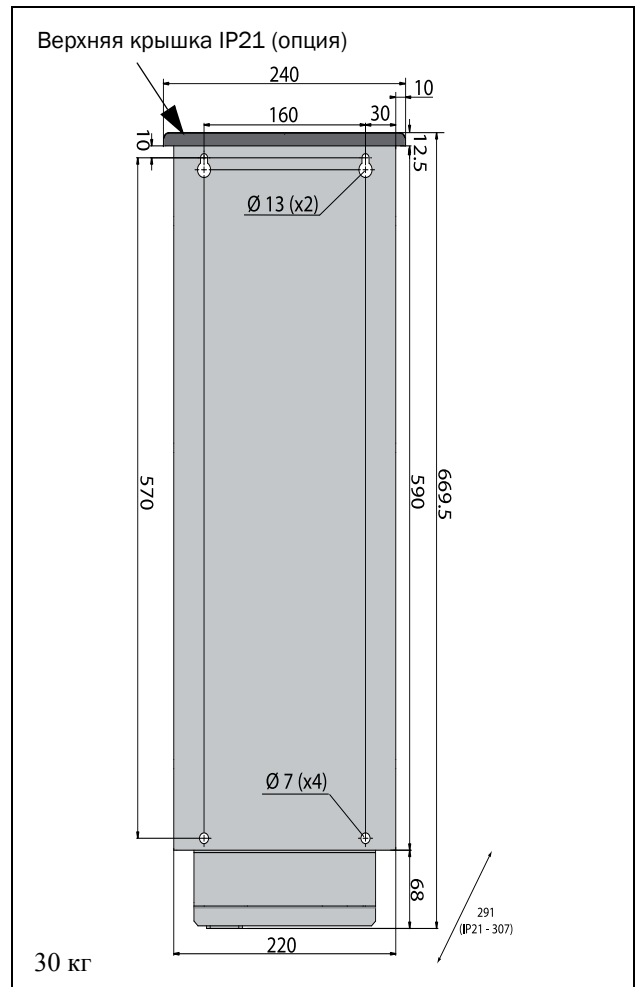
Устройство Emotron FDU моделей от 48-060 до 48-088 (типоразмер корпуса D2), вид сзади.
